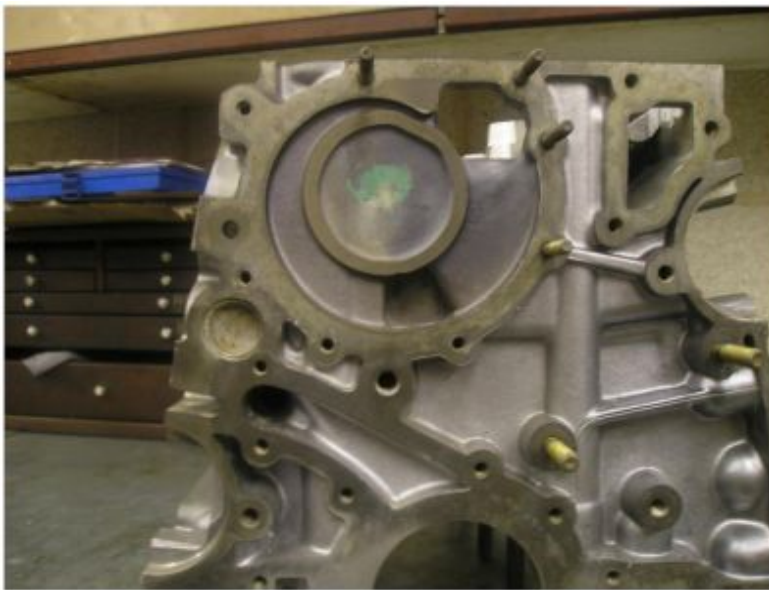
Motorblock eines Porsche 944 mit Flansch für Wasserpumpe
